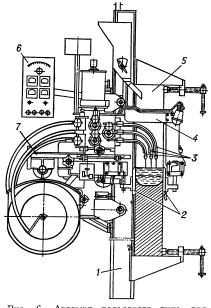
Автомат рельсового типа для электрошлаковой сварки проволочными электродами: 1— направляющий рельсэлектродами. 7— направляющий рельс-колонна, закрепляемый на изделии; 2— передний и задний ползуны; 3— токопод-водящие мундштуки с электродами; 4 пластина для крепления заднего ползуна; 5 — изделие; 6 — пульт управления; 7 горизонтальной подачи.
